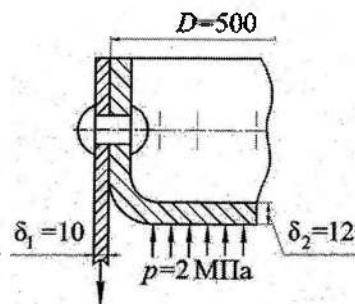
Крепление дна цилиндрического резервуара отбортовкой наружу
